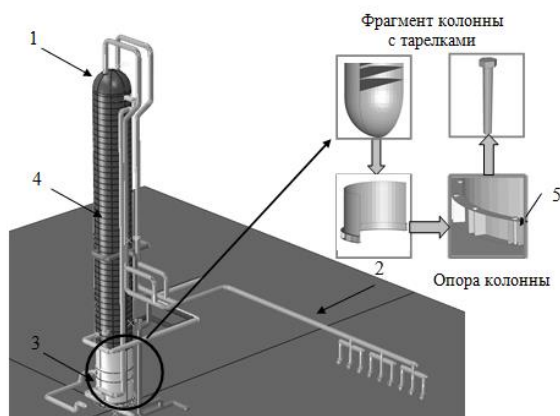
Геометрическая модель колонны: 1 – колонна, 2 – обвязка колонны, 3 – крепление колонны к фундаменту, 4 – ректификационные тарелки; 5 – анкерный болт
